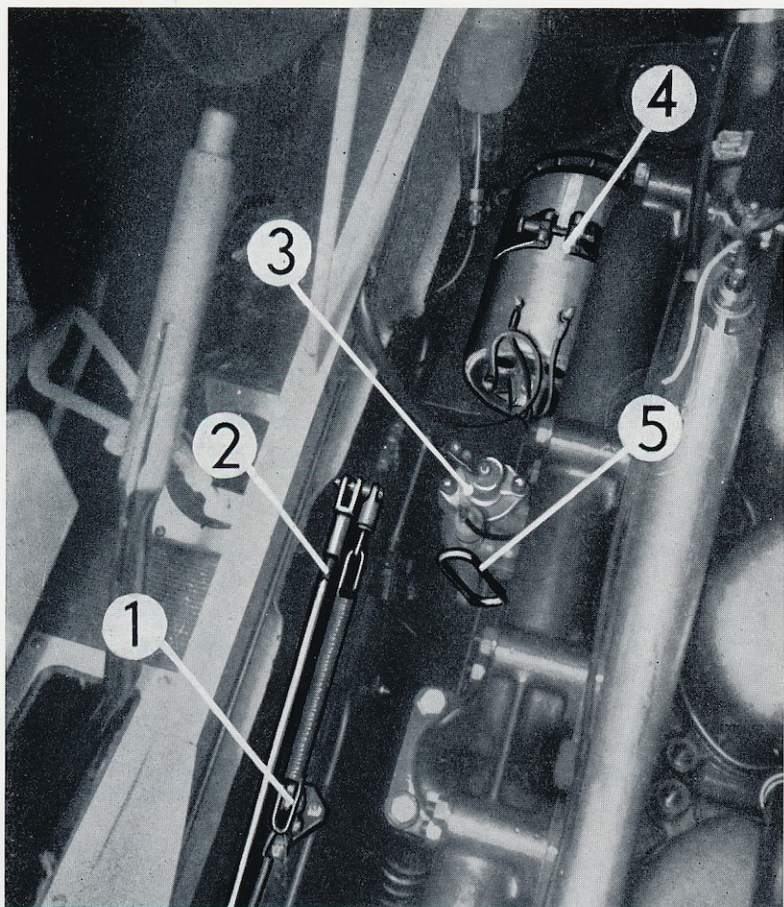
Vue du moteur capot ouvert sur cabine avancée.
